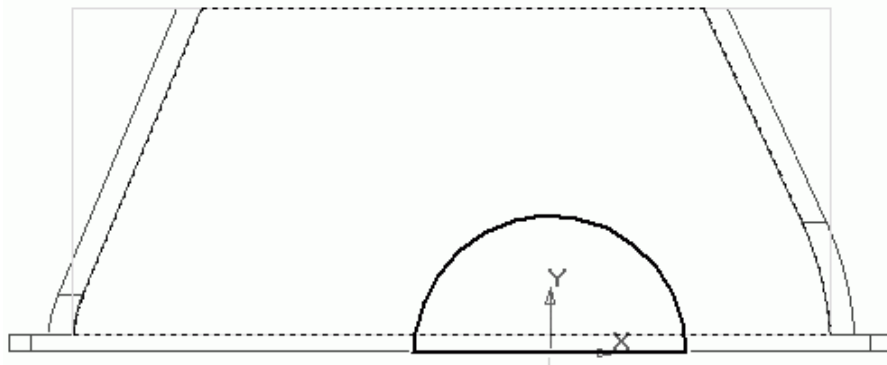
Эскиз для формирования мест крепления крышек подшипника
